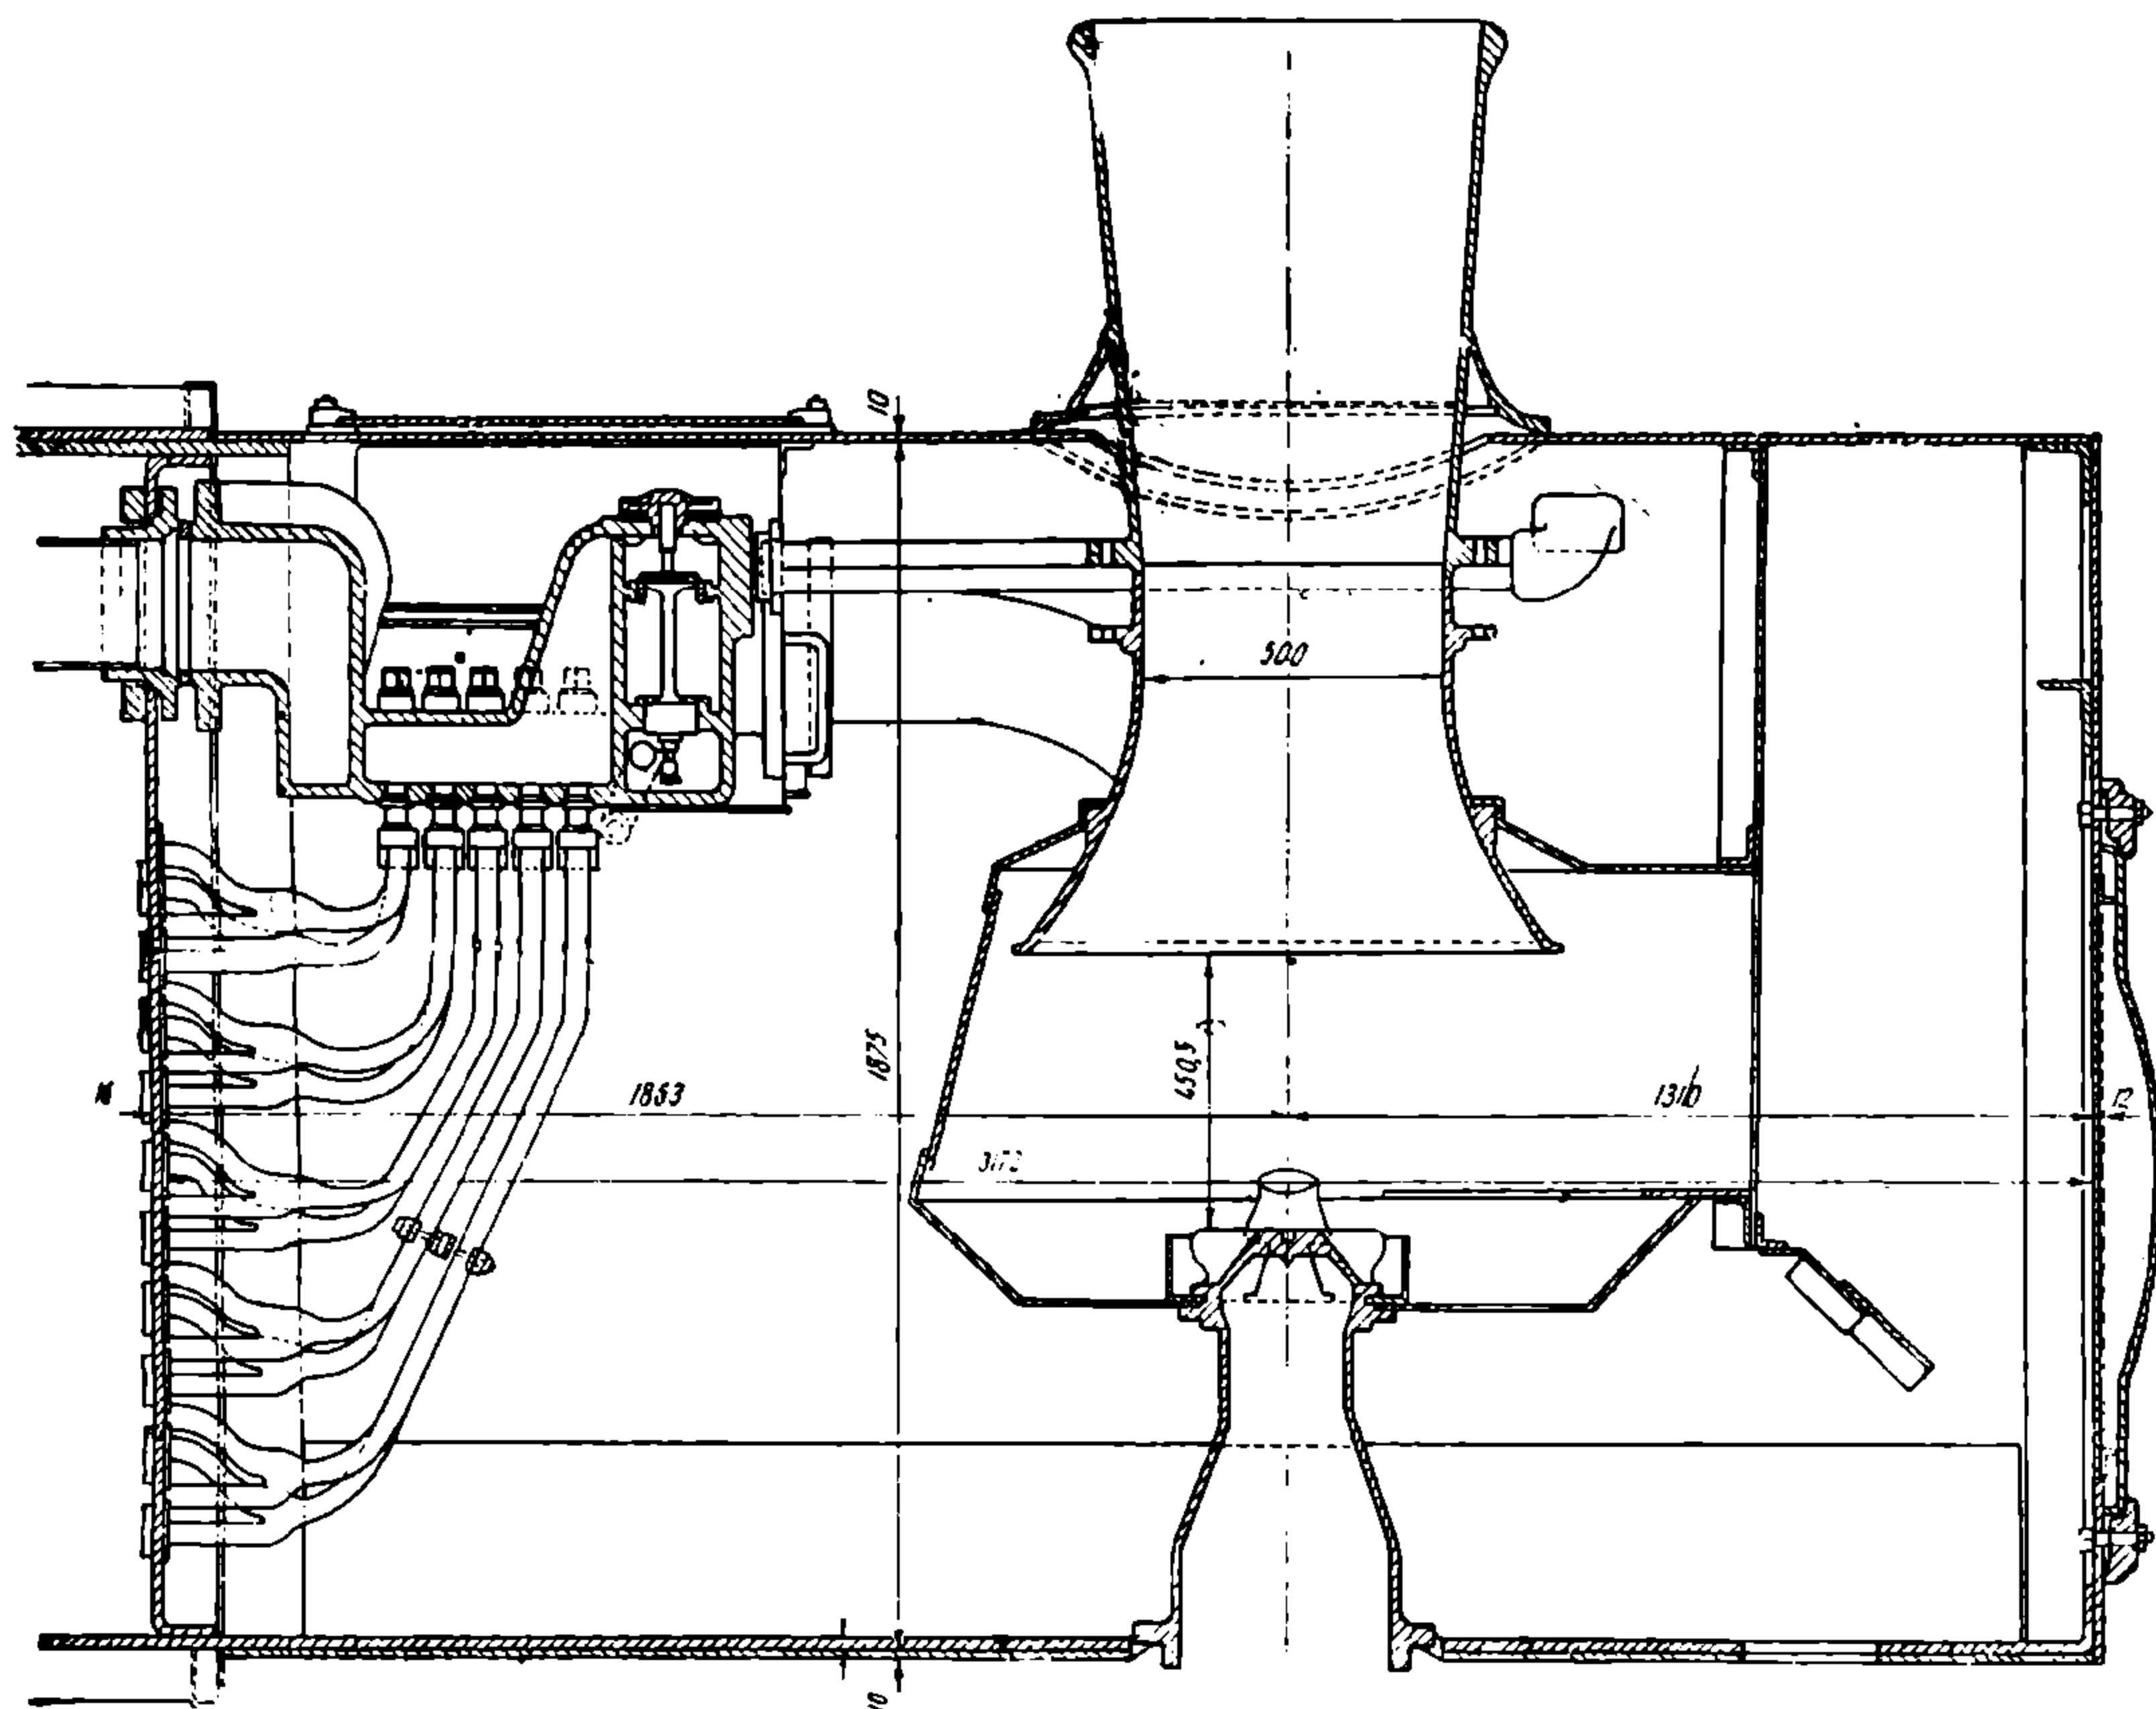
Расположение многоклапанного регулятора в дымовой коробке. Вид сверху.
